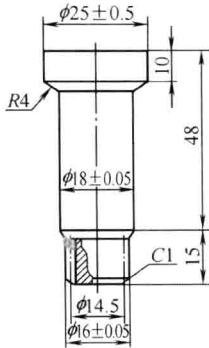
冷挤压中碳钢洗衣机齿轮轴
